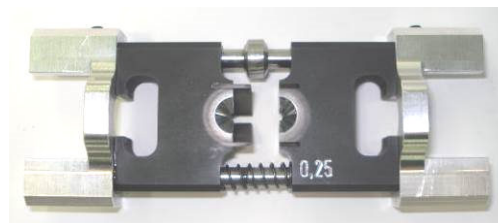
Hülsenhalteeinheit / ferrule holding unit
